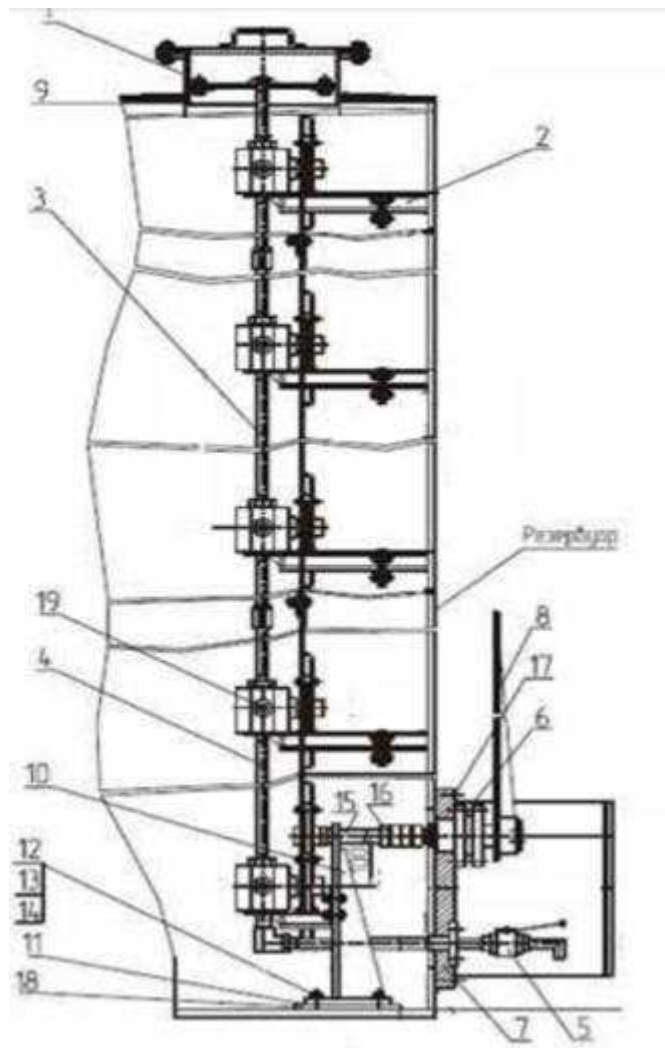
Общий вид пробоотборника секционного резервуарного типа
